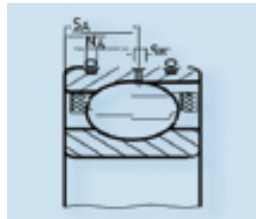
Шпиндельный подшипник конструкции DLR
